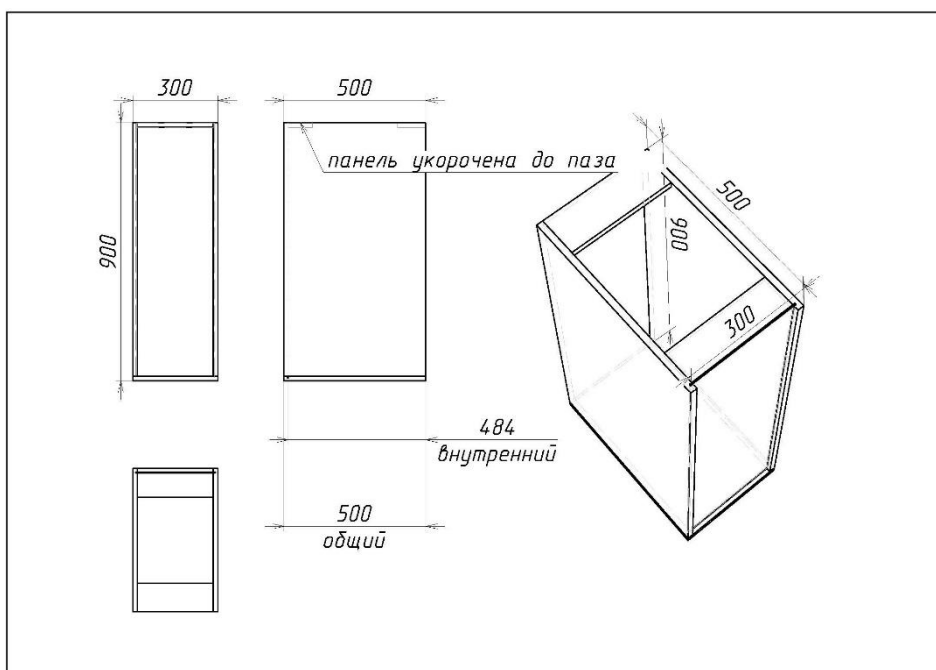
Установка задней стенки в четверть в корпус с вкладными крышкой и дном (БМ)
